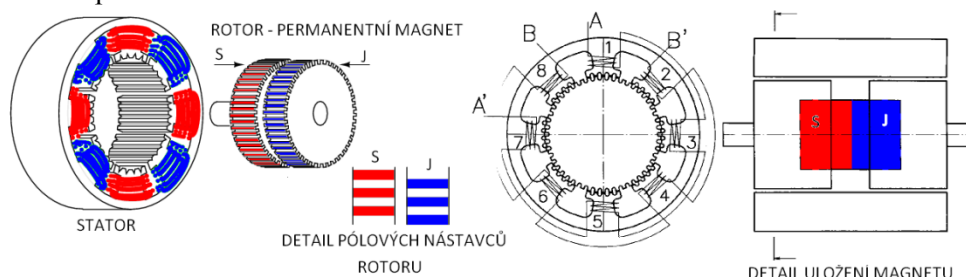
Základní princip krokového motoru s aktivním rotorem [4]
